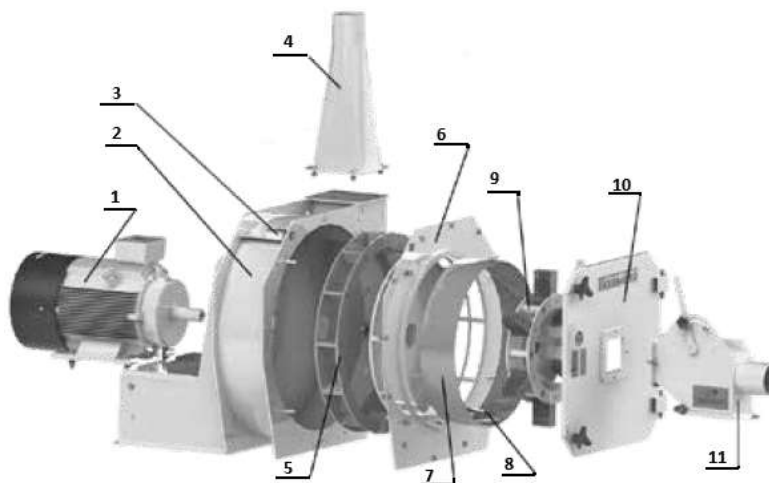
Общий вид дробилки ДКМП 2,2:
